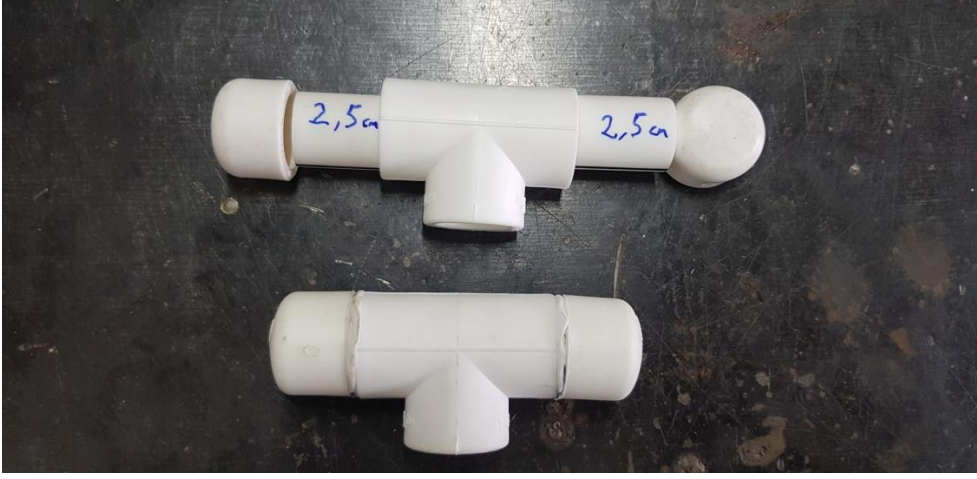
Biyofiltre su girişi fittinglerinin üst kapağa montajı (Orijinal).
